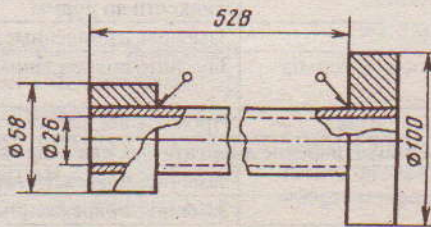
Подставка для запрессовки среднего подшипника с подушкой в сборе
